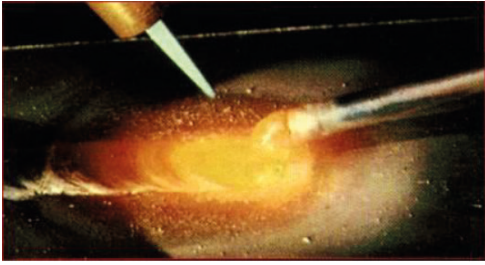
Sağ ve sol kaynak işleminde üflece verilecek açılar
